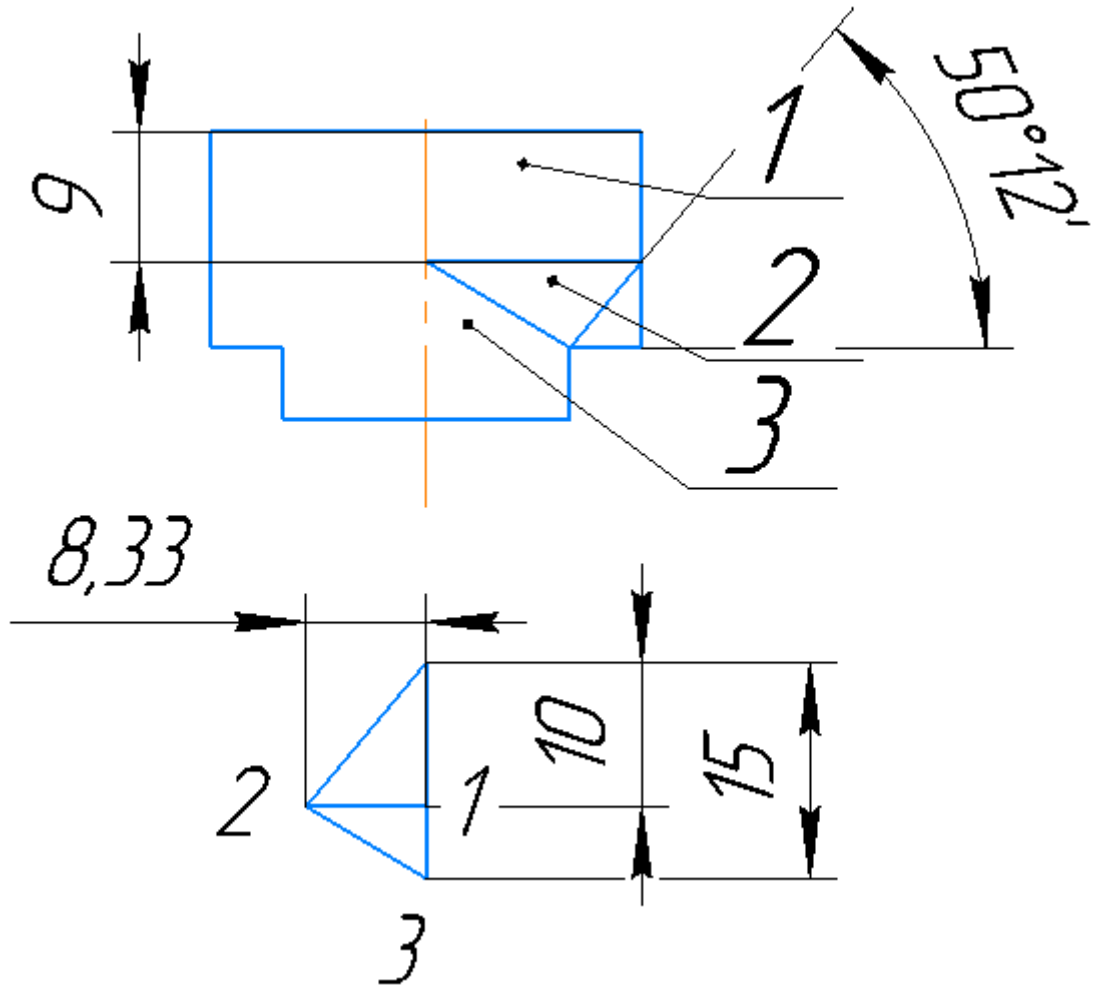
Розрахункова схема(кут 50) та план швидкостей
